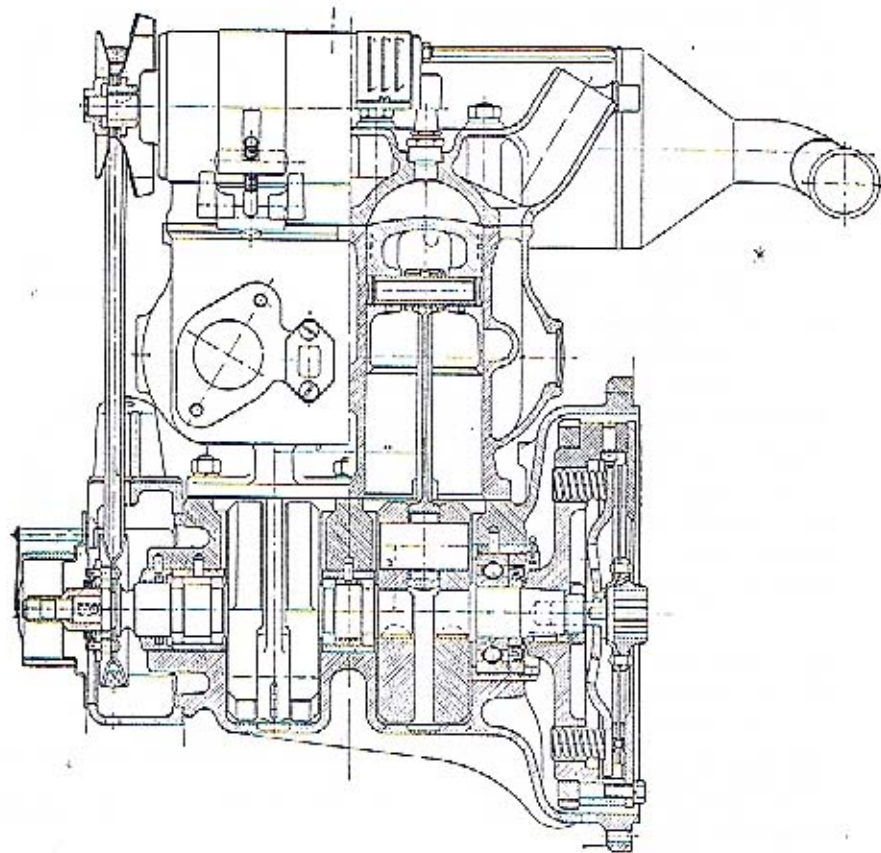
Řez dvoudobým motorem s vratným vyplachováním (motor Jawa)
